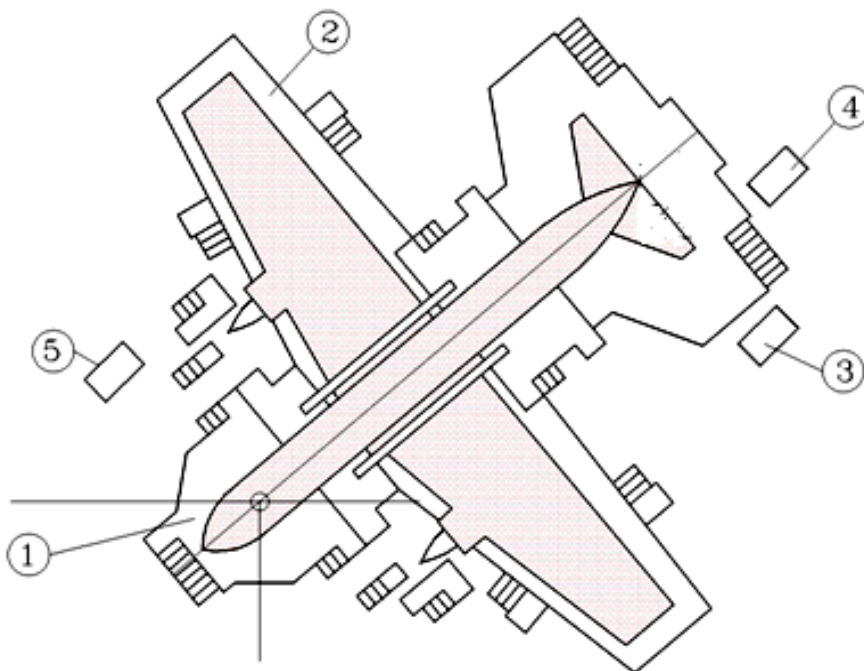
Стенд предъявления представителю заказчика ЭРАНО, чистоты, залочки, опрессовки, нивелировки и передачи на ЛИС: 1 – стремянки фюзеляжные; 2 – стремянки подкрыльевые; 3 – стенд для испытаний фюзеляжа на герметичность и прочность; 4 – вихревая установка; 5 – стенд комплексной отработки гидросистемы
